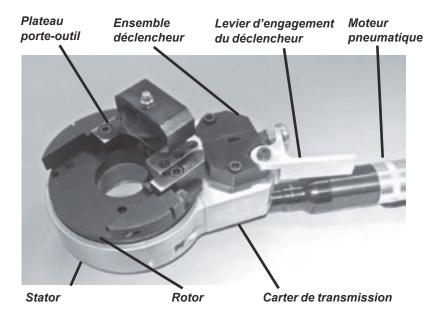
Cette photo illustre les principaux composants de la machine SDSF.
